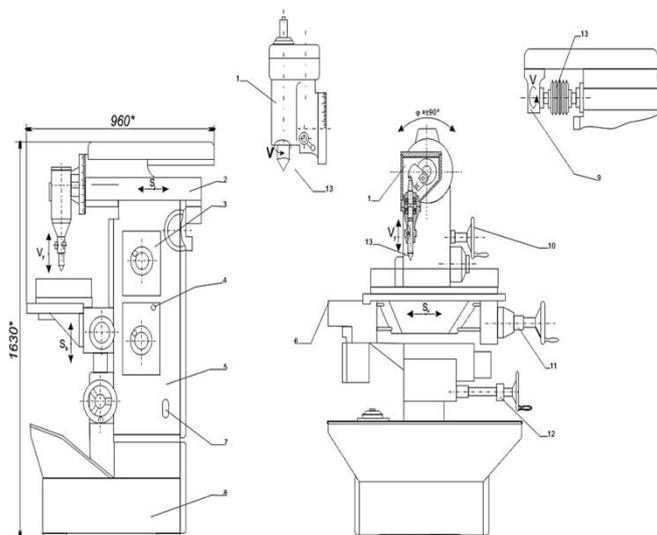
Общий вид виброударного станка для отделения отливок от литейных блоков.
